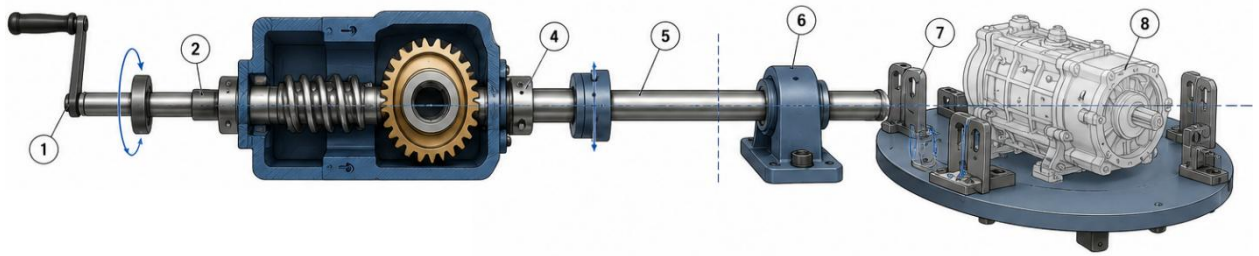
Кінематична схема механізму повороту КПП:
